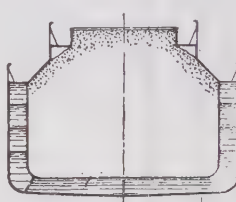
Barco con cubierta elevada, principalmente para el transporte de mineral
